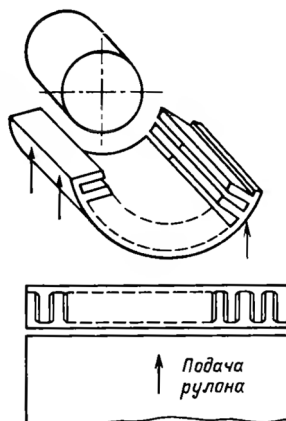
Згортання плоского шихтованого пакета в циліндр
